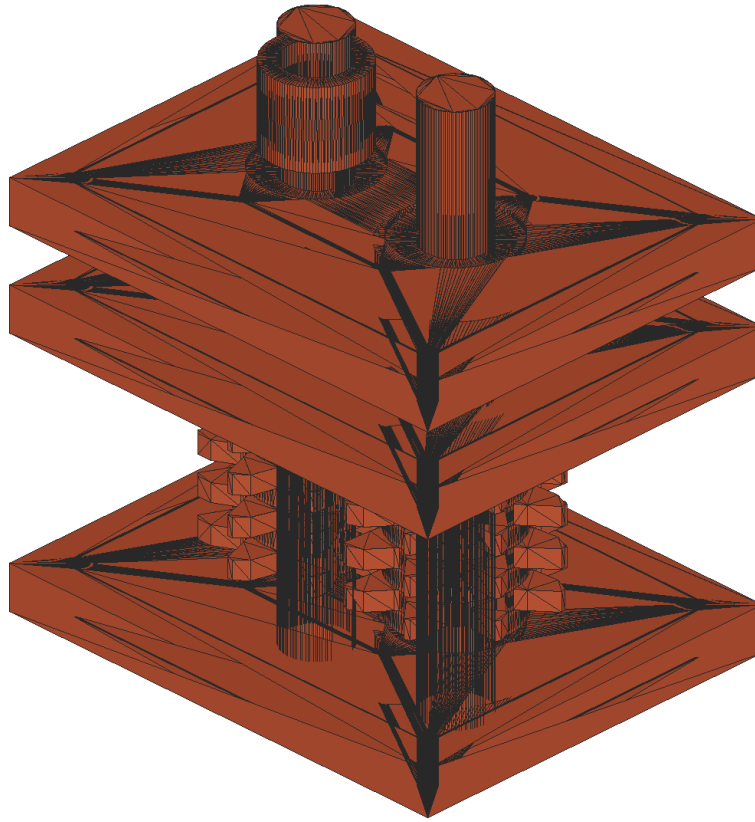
Stage 1 proof — hopper/chamber containment와 실제 gear tooth는 별도 상세 필요
